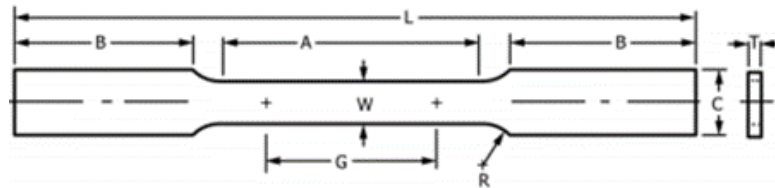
Adaptado do modelo “gravata” para ensaio de tração
